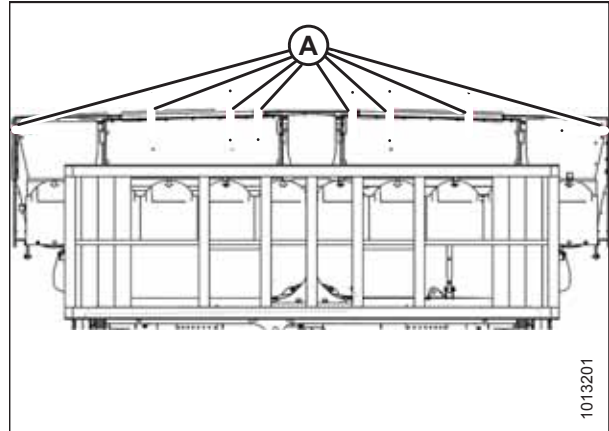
Vu du dessous du faucheur à disques de type tracté
